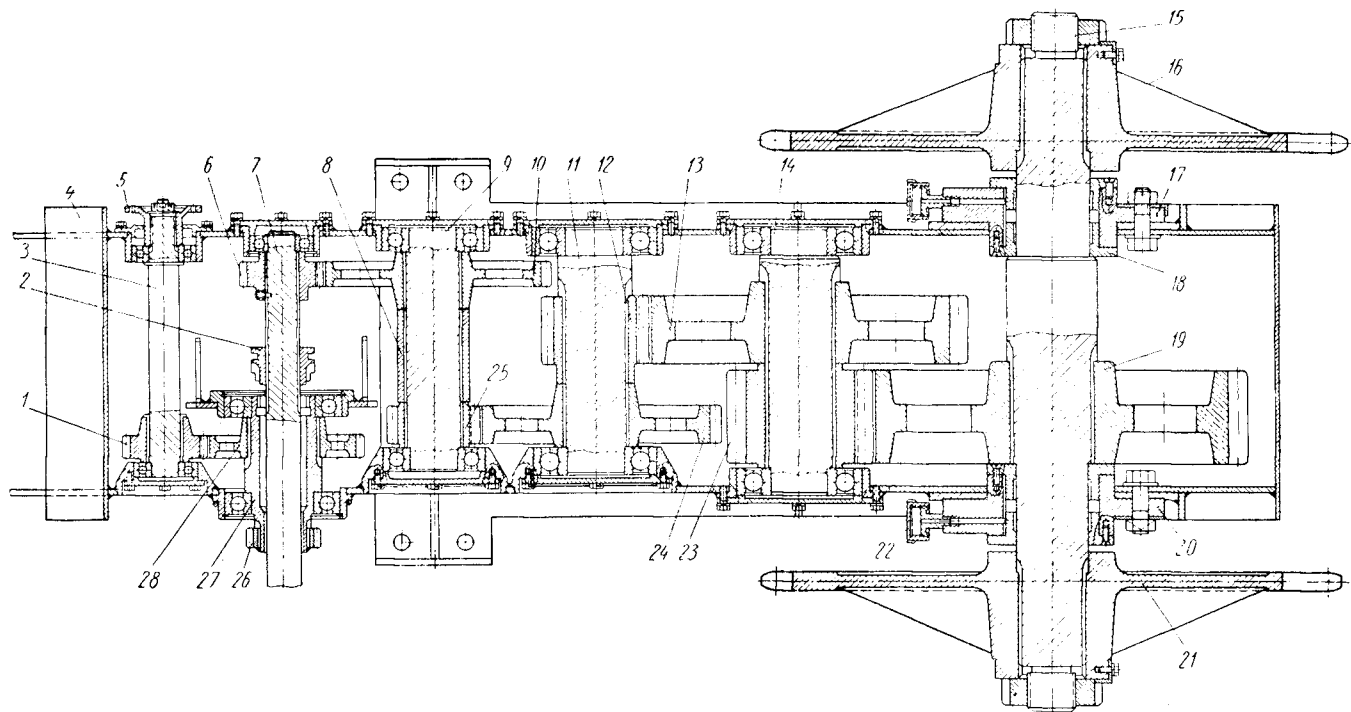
Бортовой редуктор экскаватора-каналокопателя Д-583:
